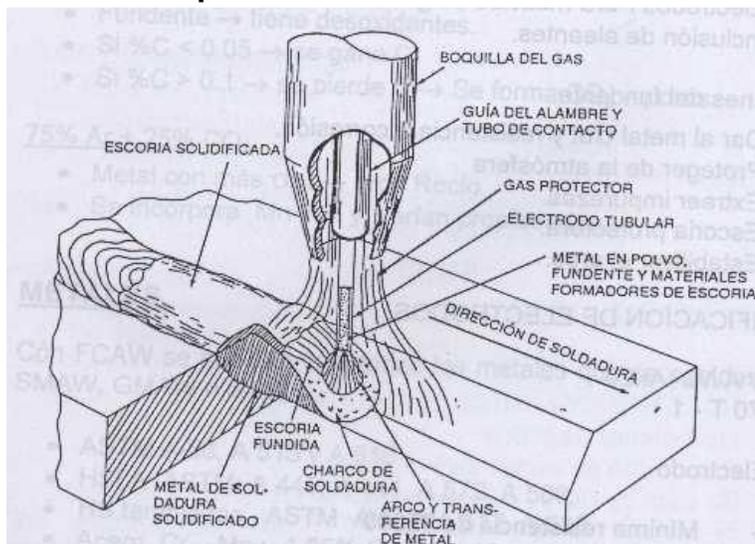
Soldadura eléctrica por arco con alambre tubular como electrodo FCAW¹⁹
